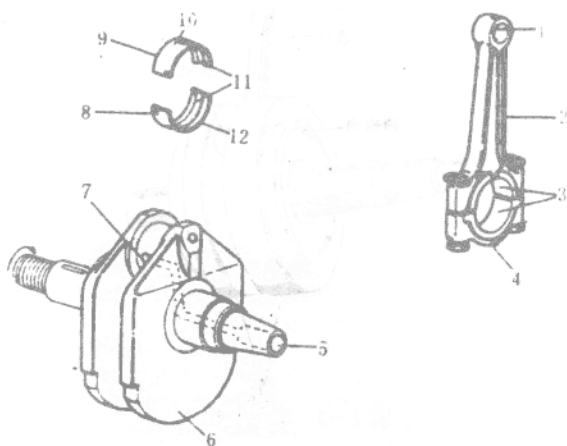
装滑动轴承的曲轴,由整体铸钢件加工而成
